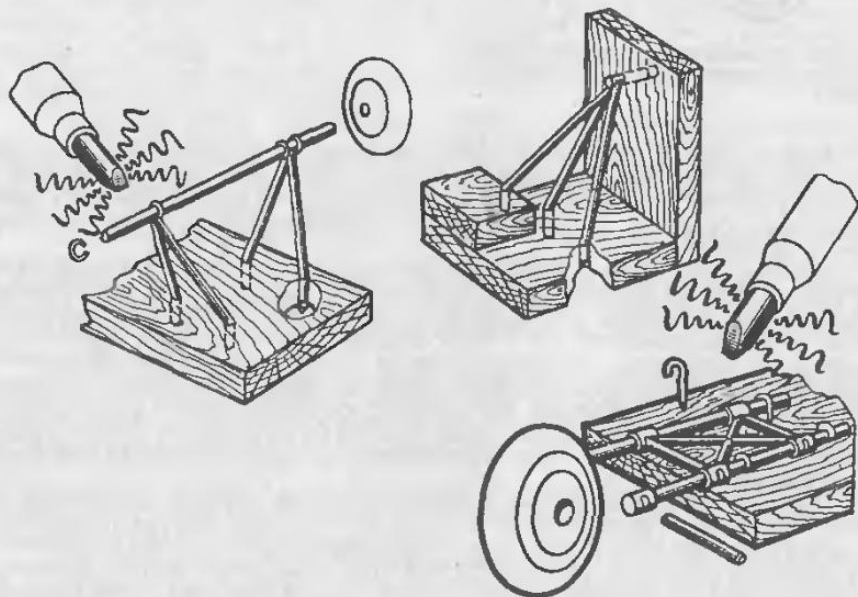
Образцы приспособлений для пайки пространственных конструкций шасси
